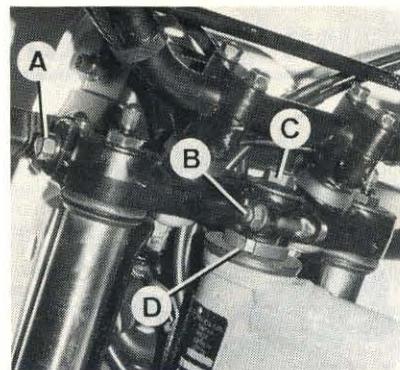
Jeu à la direction A. et B. Vis et boulon de bridage - C. Vis supérieure - D. Écrou crénelé de réglage (Photo RMT)
